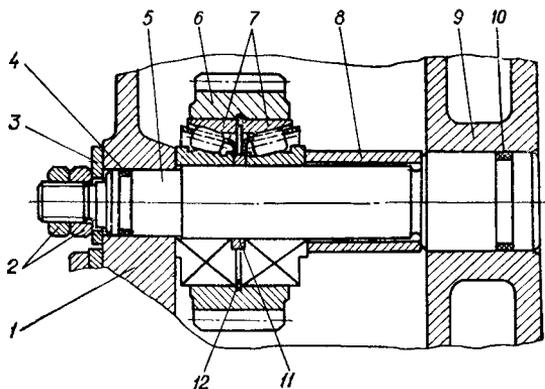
Разрез по оси промежуточной шестерни реверс-редуктора:
